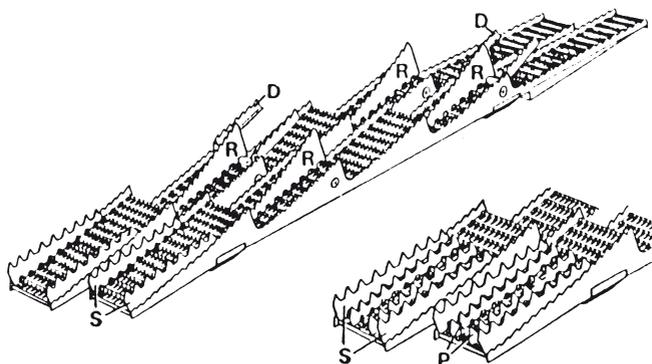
Клавиши соломотряса с дополнительными приспособлениями для рыхления соломы различных типов (S, D, R, P).
